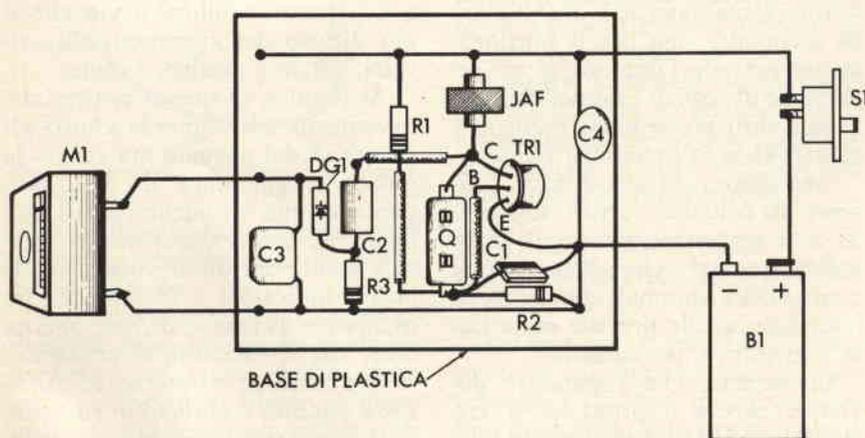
Schema di cablaggio del provacristalli; come è detto nel testo la maggior parte dei componenti è montata sopra una base in plastica.
